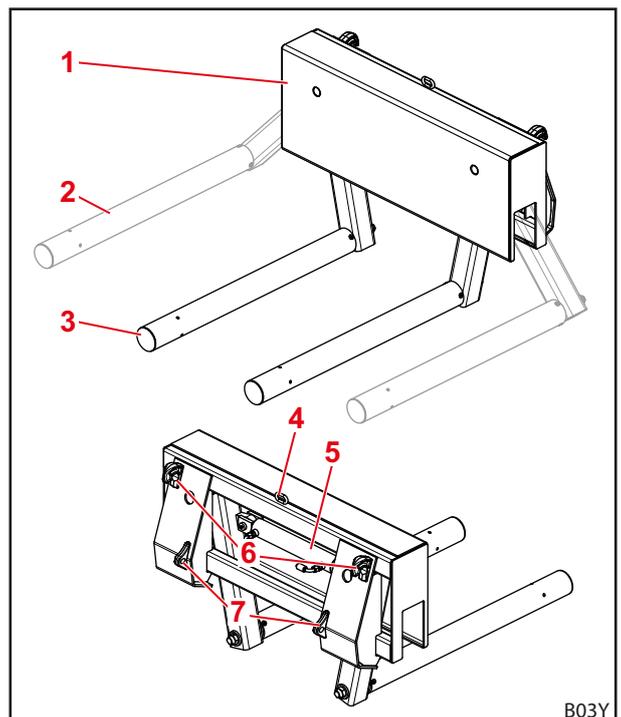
Struttura forca per rotoballe a sezione cilindrica
